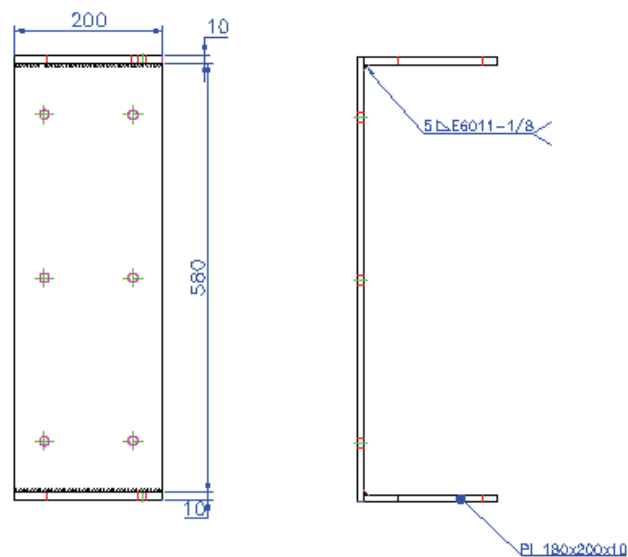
Dimensiones de la soldadura a corte.
